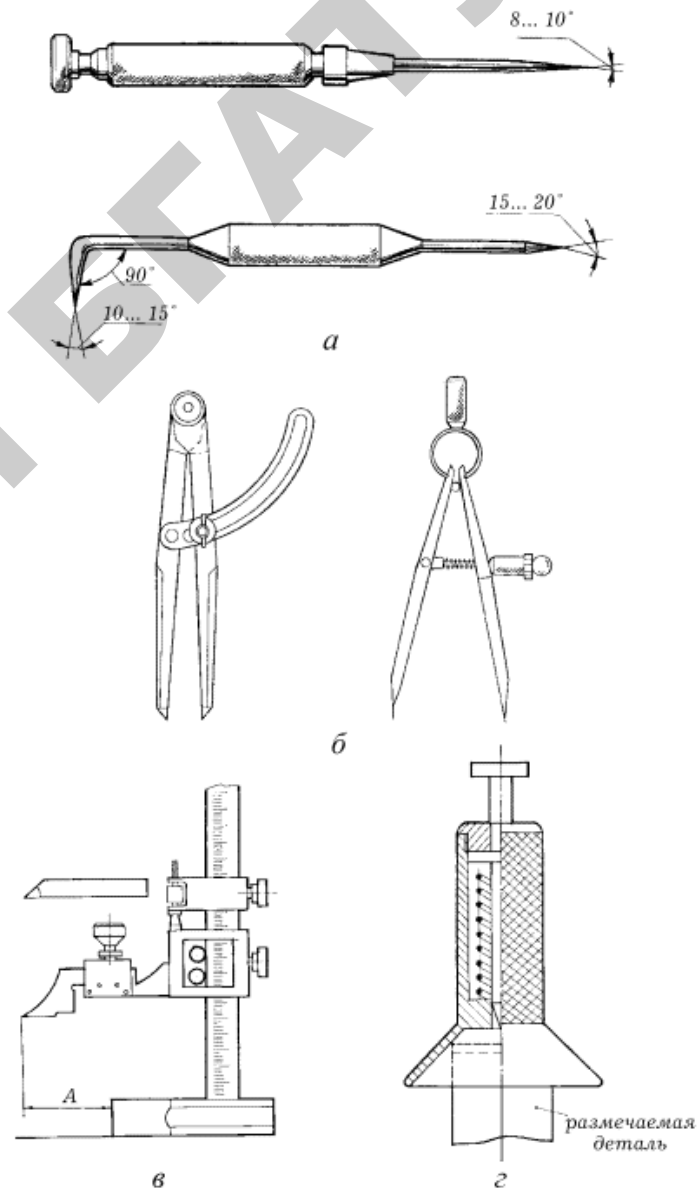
Разметочные инструменты: *a* – чертилки; *б* – циркули; *в* – штангенрейсмус; *г* – кернер-центроискатель
